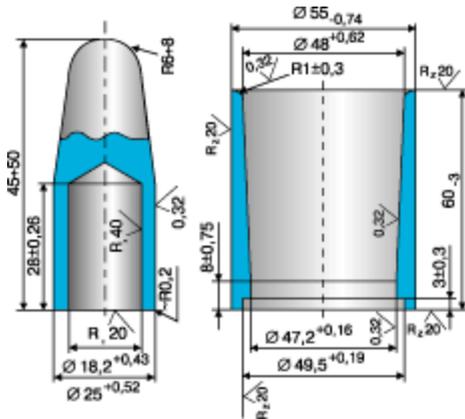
Конусные оправки для установки манжеты и уплотнительного кольца в резервуар
